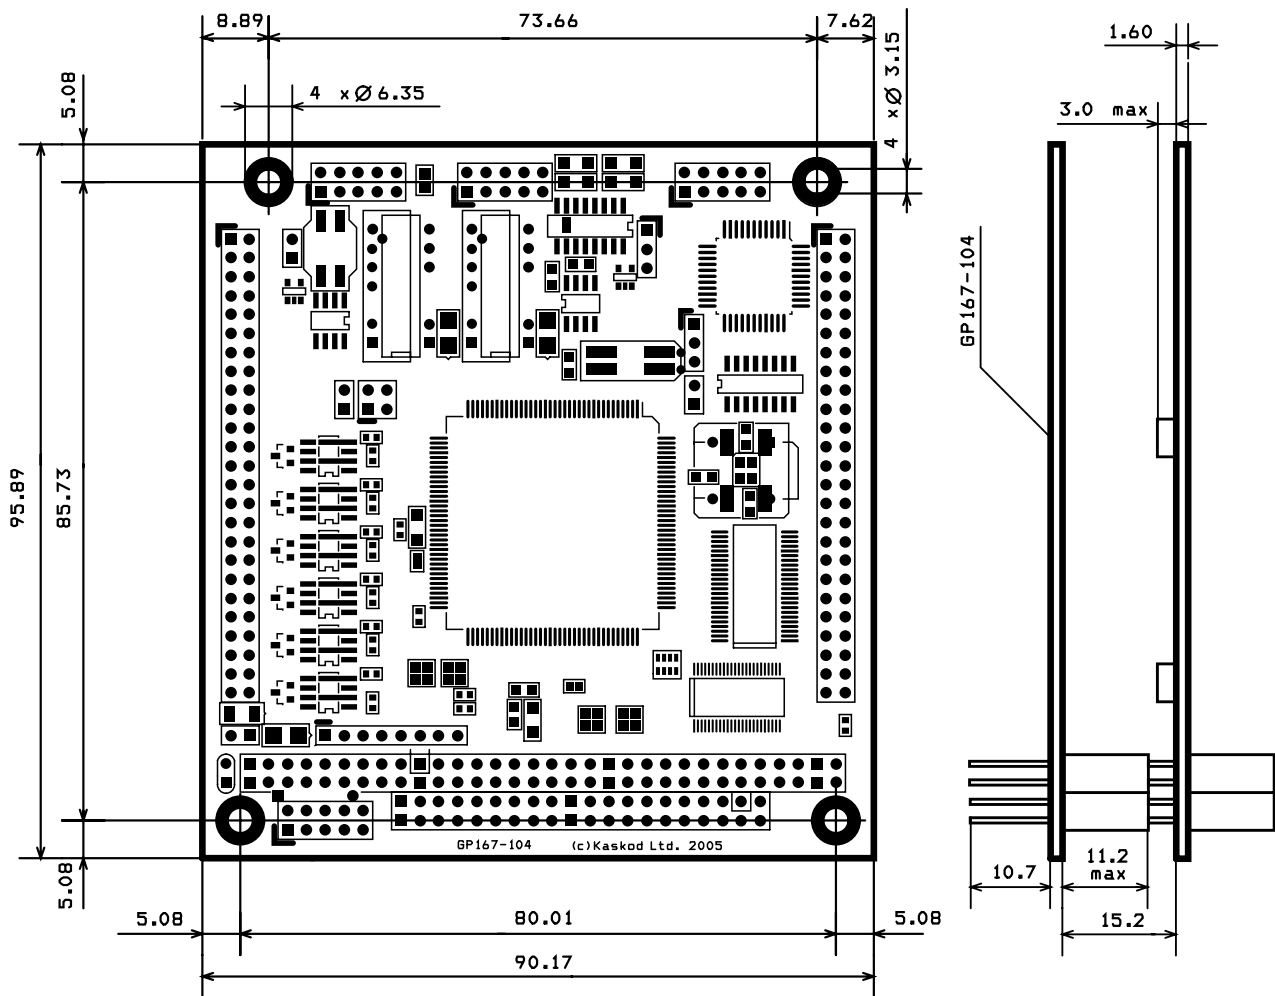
Габаритные и установочные размеры в миллиметрах.
